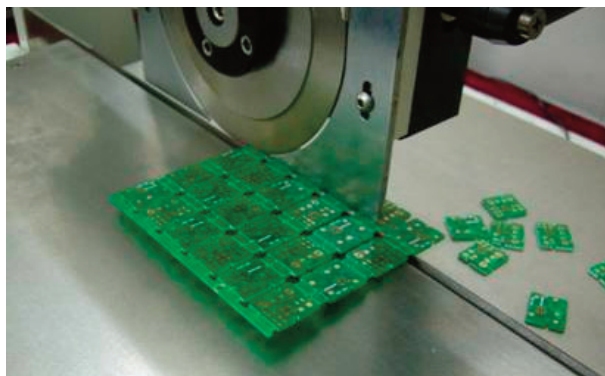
Zum Teilen von PCB-Platinen verwendete V-Schnitt-Maschine
